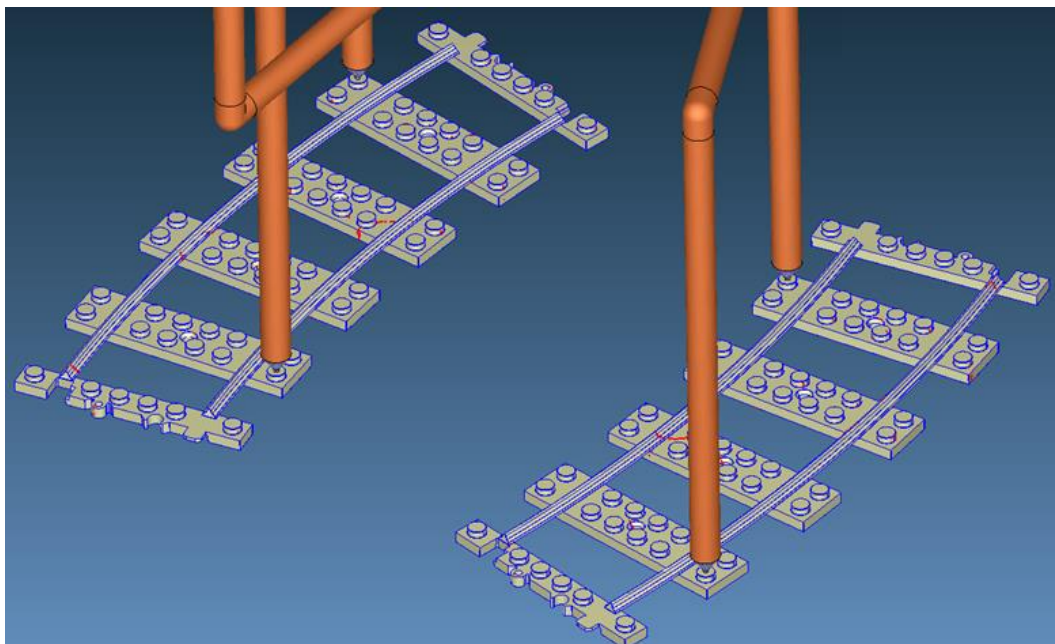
Líneas de soldadura de la 1ª inyección
